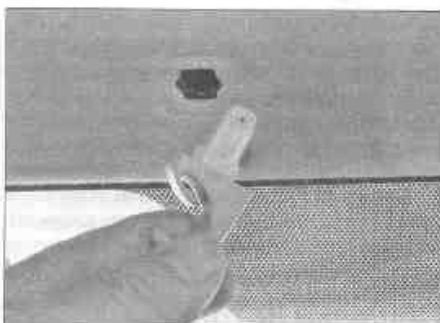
Поверните установочный фиксатор, чтобы снять
